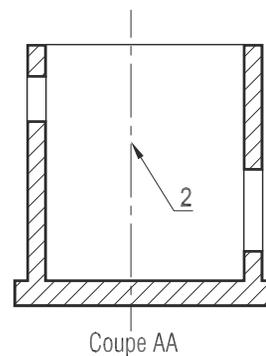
principe de la coupe brisée, coupe à plans parallèles
